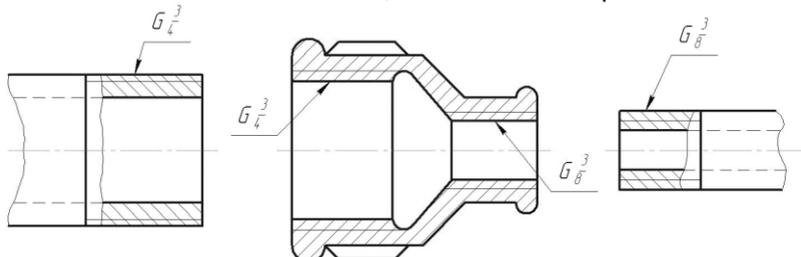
Обозначение трубной цилиндрической резьбы
